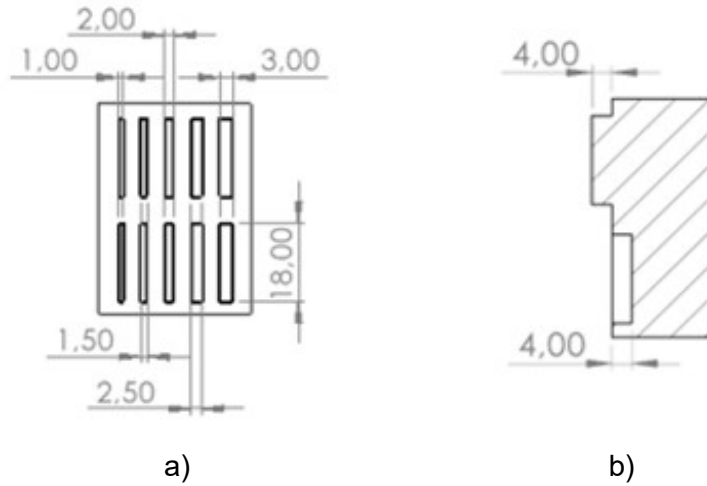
Geometría de los elementos finos (a) Planta (b) Perfil.
